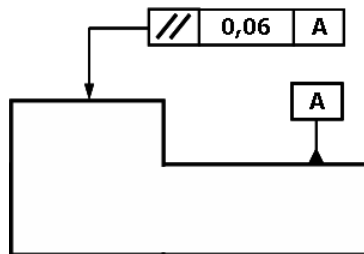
Indicação de tolerância de paralelismo em desenho técnico
